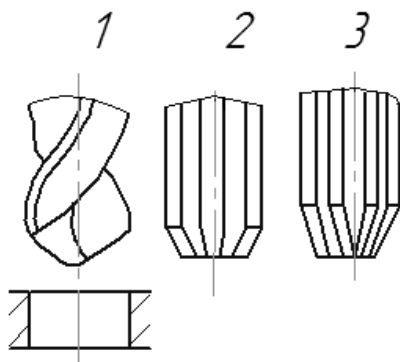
Обробка отвору трьома різними інструментами за три переходи
